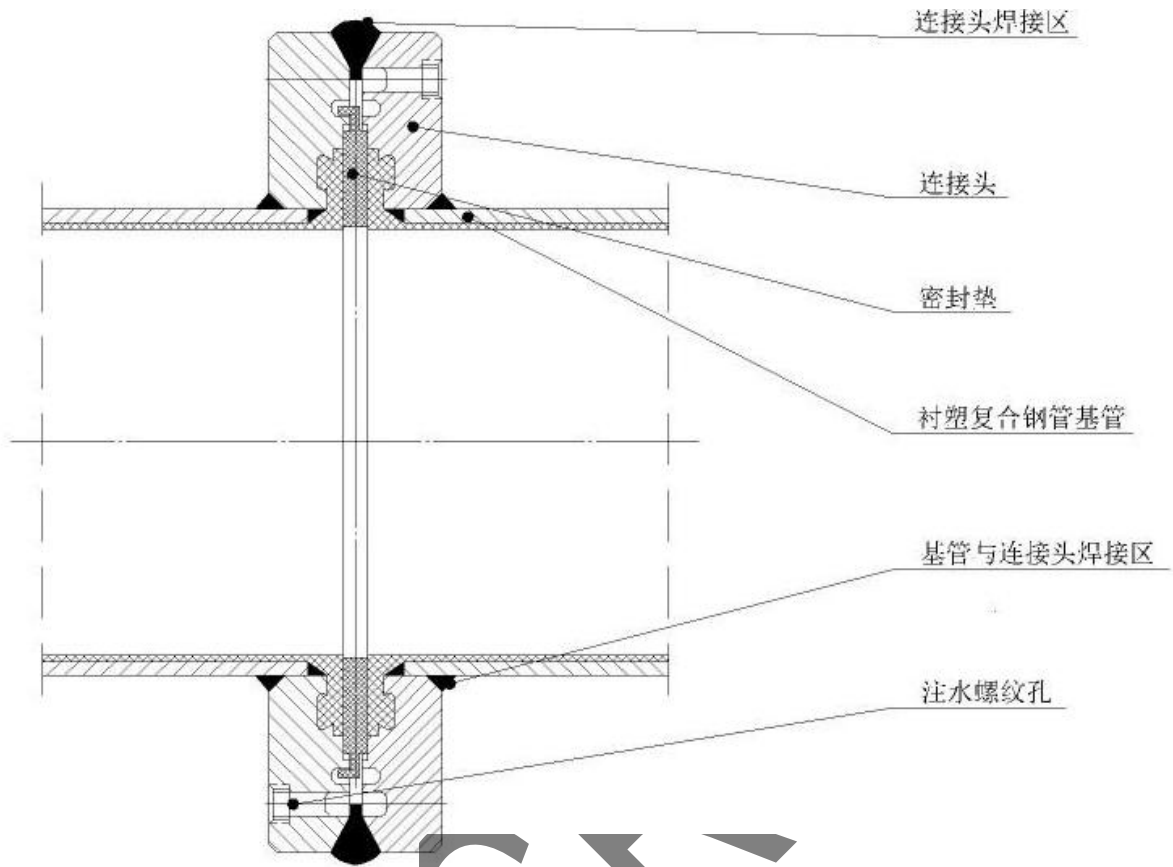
全防腐钢塑复合管对焊突缘连接结构示意图
